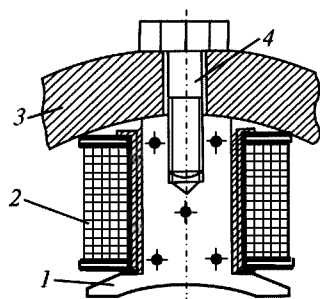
Главный полюс: 1 — сердечник главного полюса; 2 — обмотка возбуждения; 3 — станина; 4 — болт
